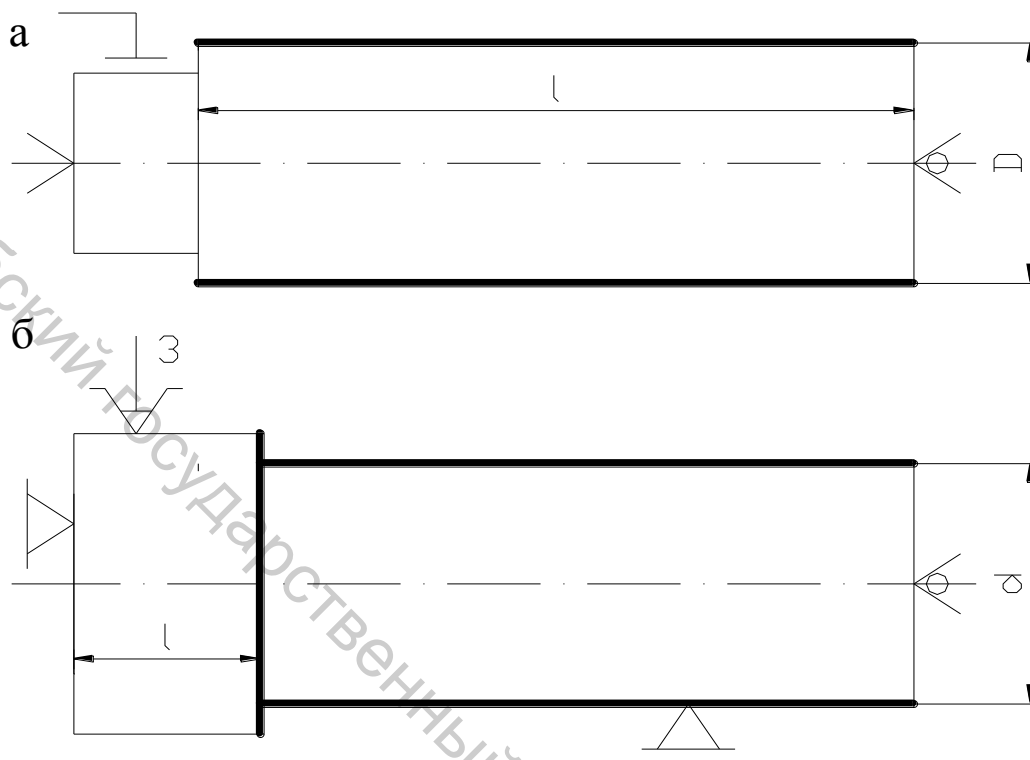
Схемы установки цилиндрических заготовок:
